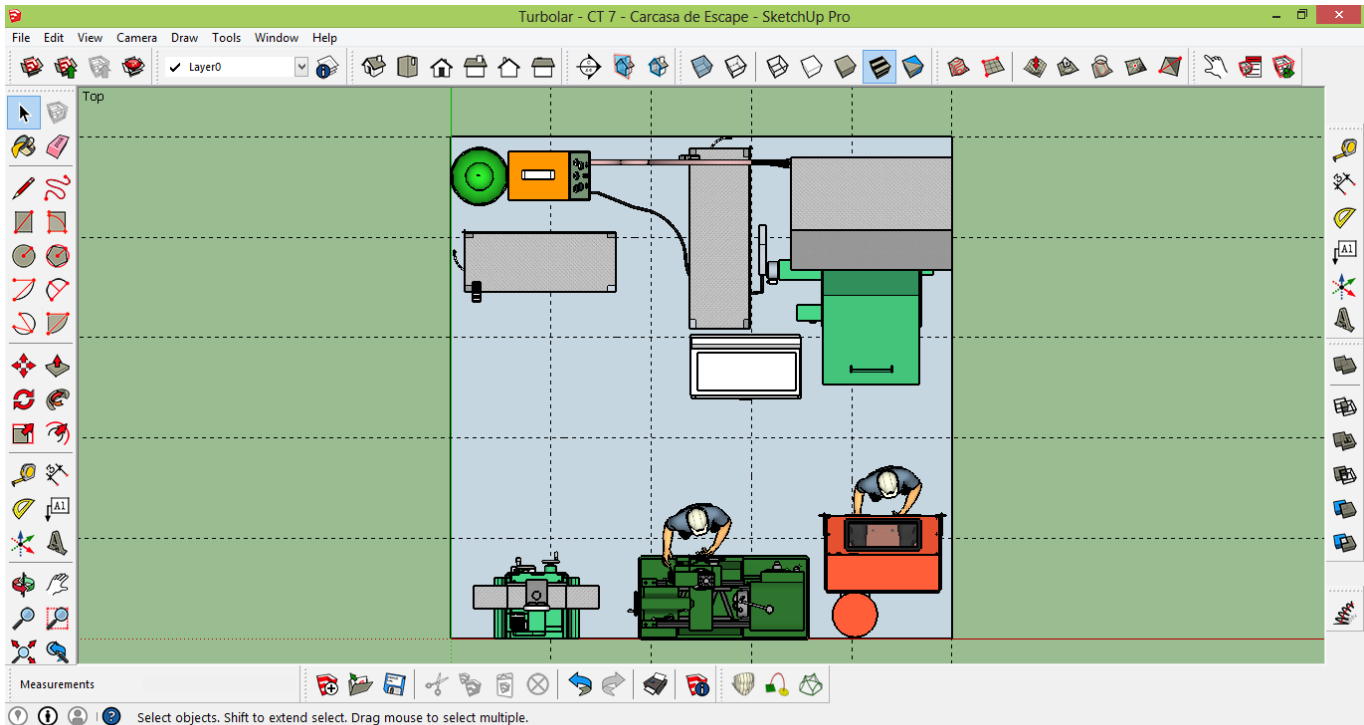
CT 7 – Carcasa de Escape – Vista Superior
